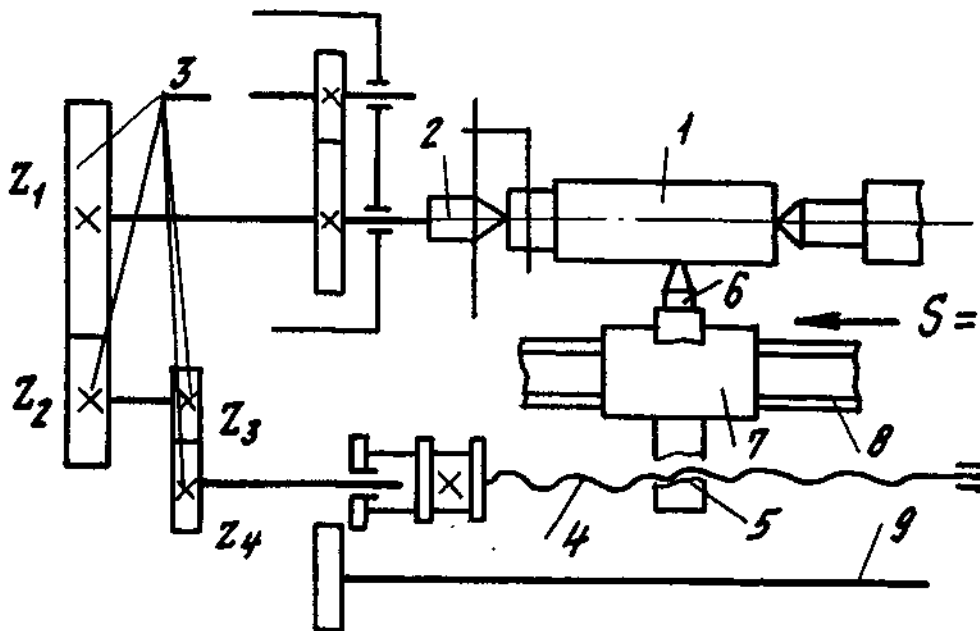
Схема нарезания резьбы резцом на токарно – винторезном станке.
